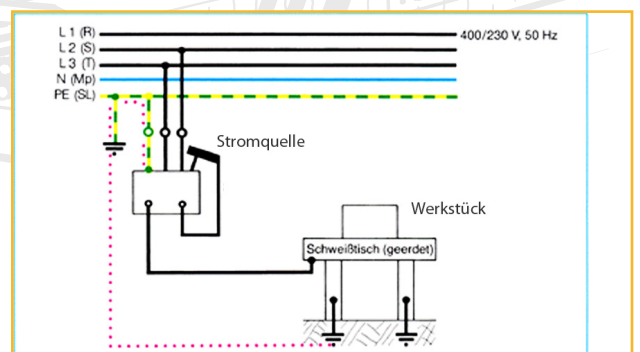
Beim nicht isolierten Ablegen des Stabelektrodenhalters auf die Schweißstromquelle kann deren Schutzleiter auch dann durchschmelzen, wenn das Werkstück oder der Schweißstisch auch ohne Elektrowerkzeug eine Erdverbindung besitzt. Der Weg des vagabundierenden Schweißstromes ist punktiert.
